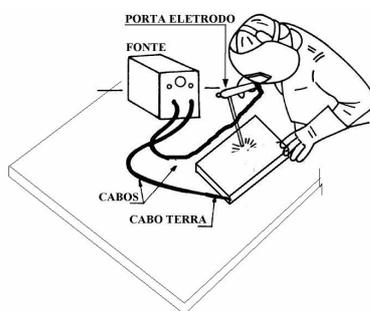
Esquema da bancada de ensaio do processo de soldagem com eletrodo revestido
